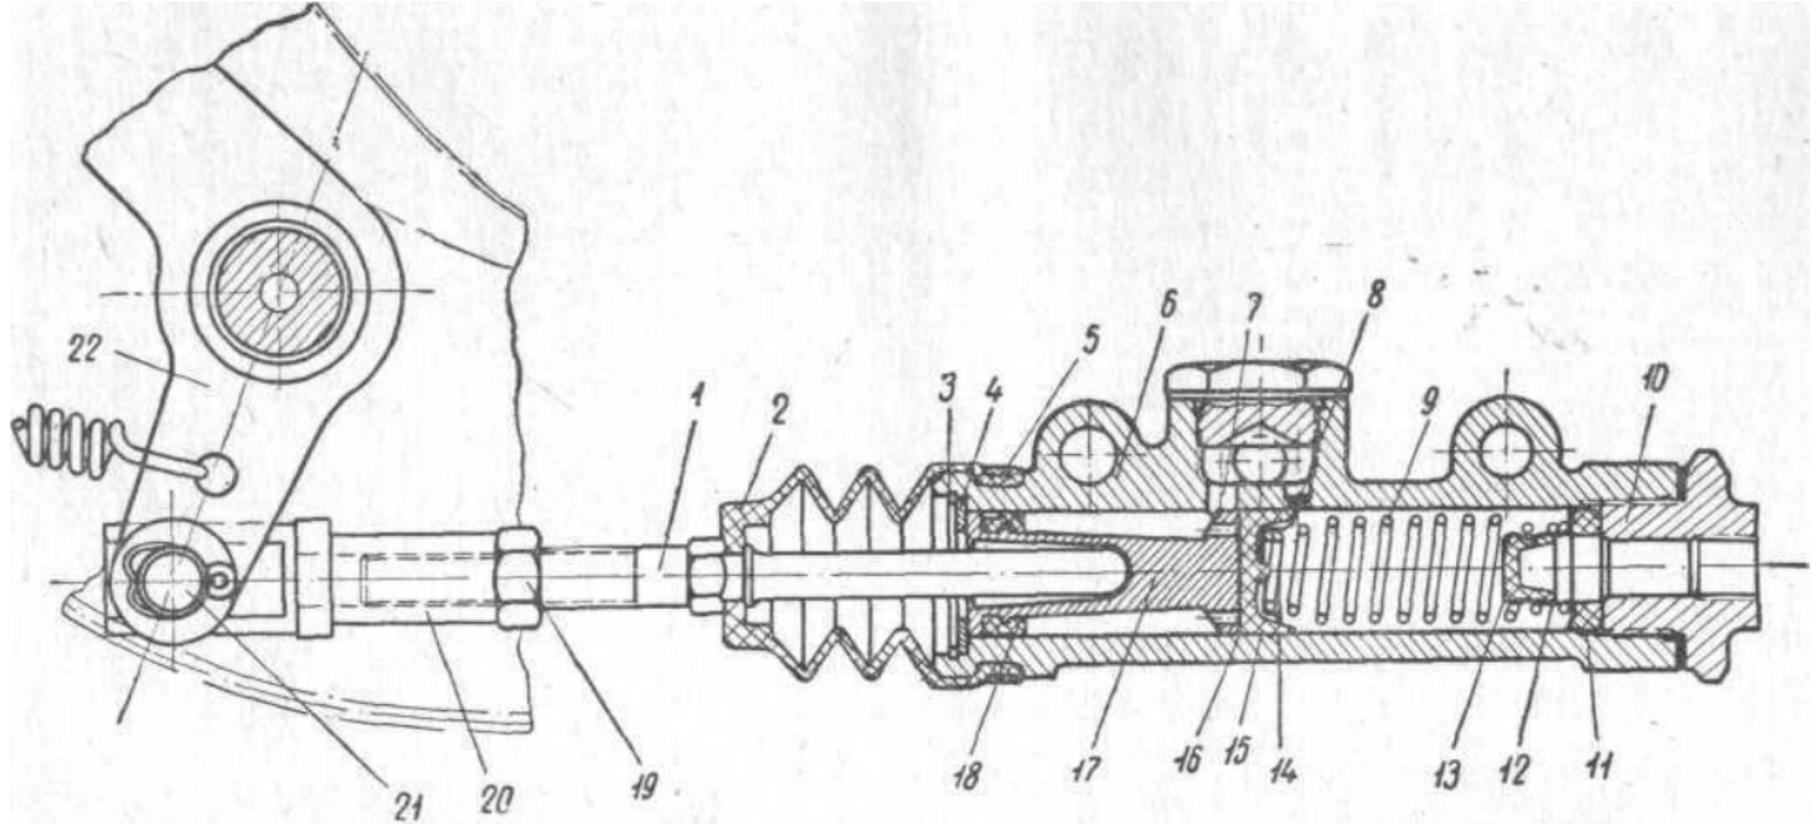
Главный тормозной цилиндр автомобиля модели 407:
